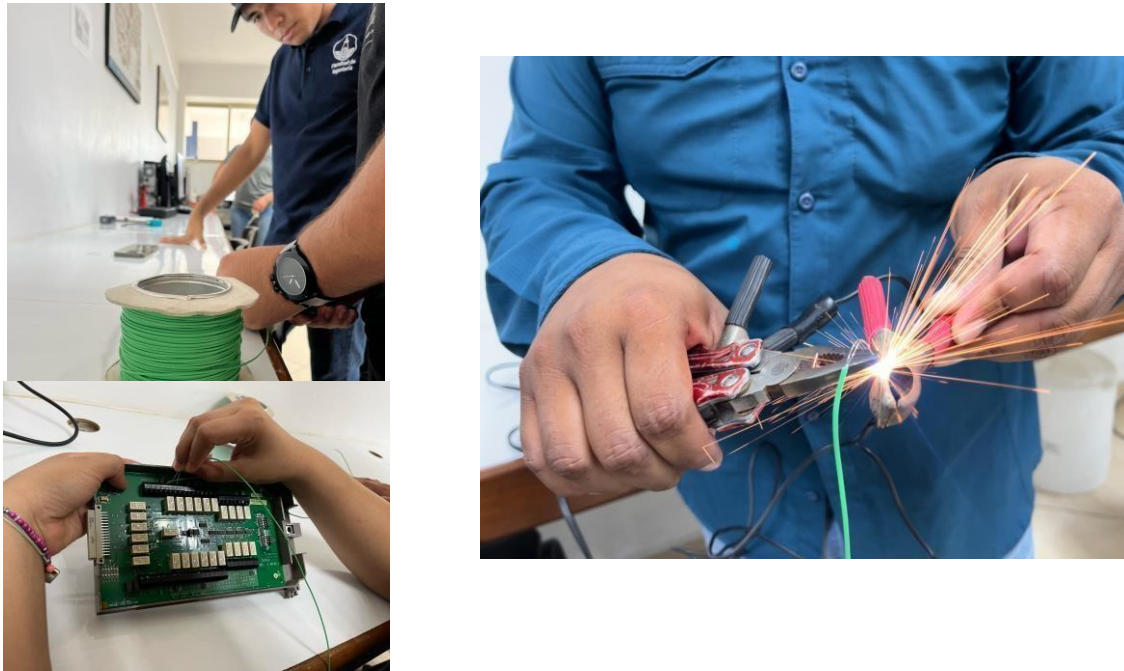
Medición, corte y soldadura del termopar
